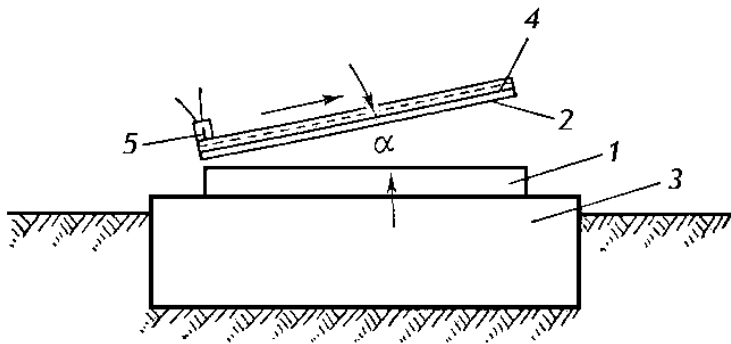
Сварка взрывом, где 1 – неподвижная деталь (мишень); 2 – подвижная (метаемая) деталь; 3 – опорная плита; 4 – заряд; 5 – детонатор
